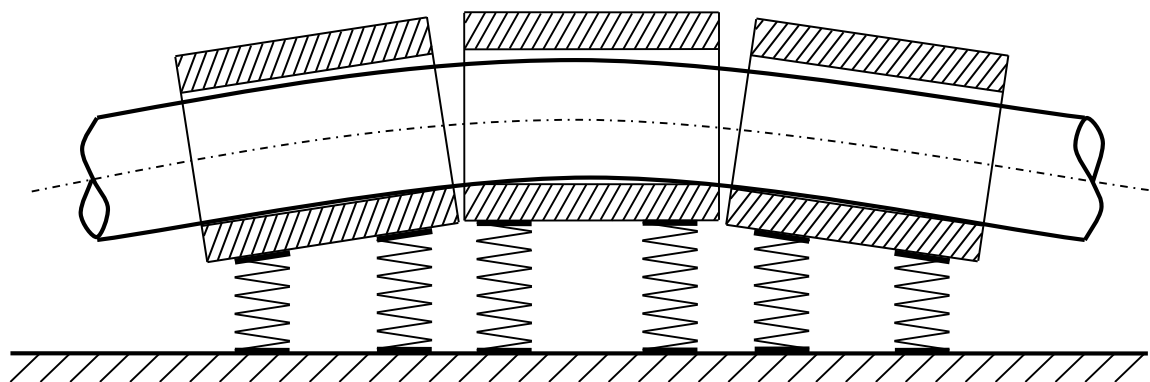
Конструктивное исполнение самоустанавливающегося подшипника
